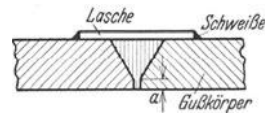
Gußschweiße mit Verstärkungslasche.
